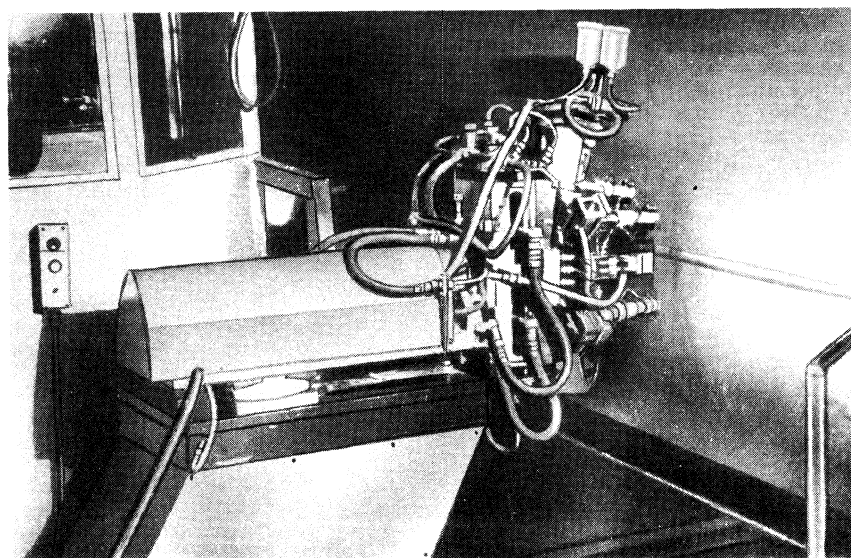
Автоматизированная установка НК-106 для ультразвукового контроля продольных сварных швов газонефтепроводных труб большого диаметра
